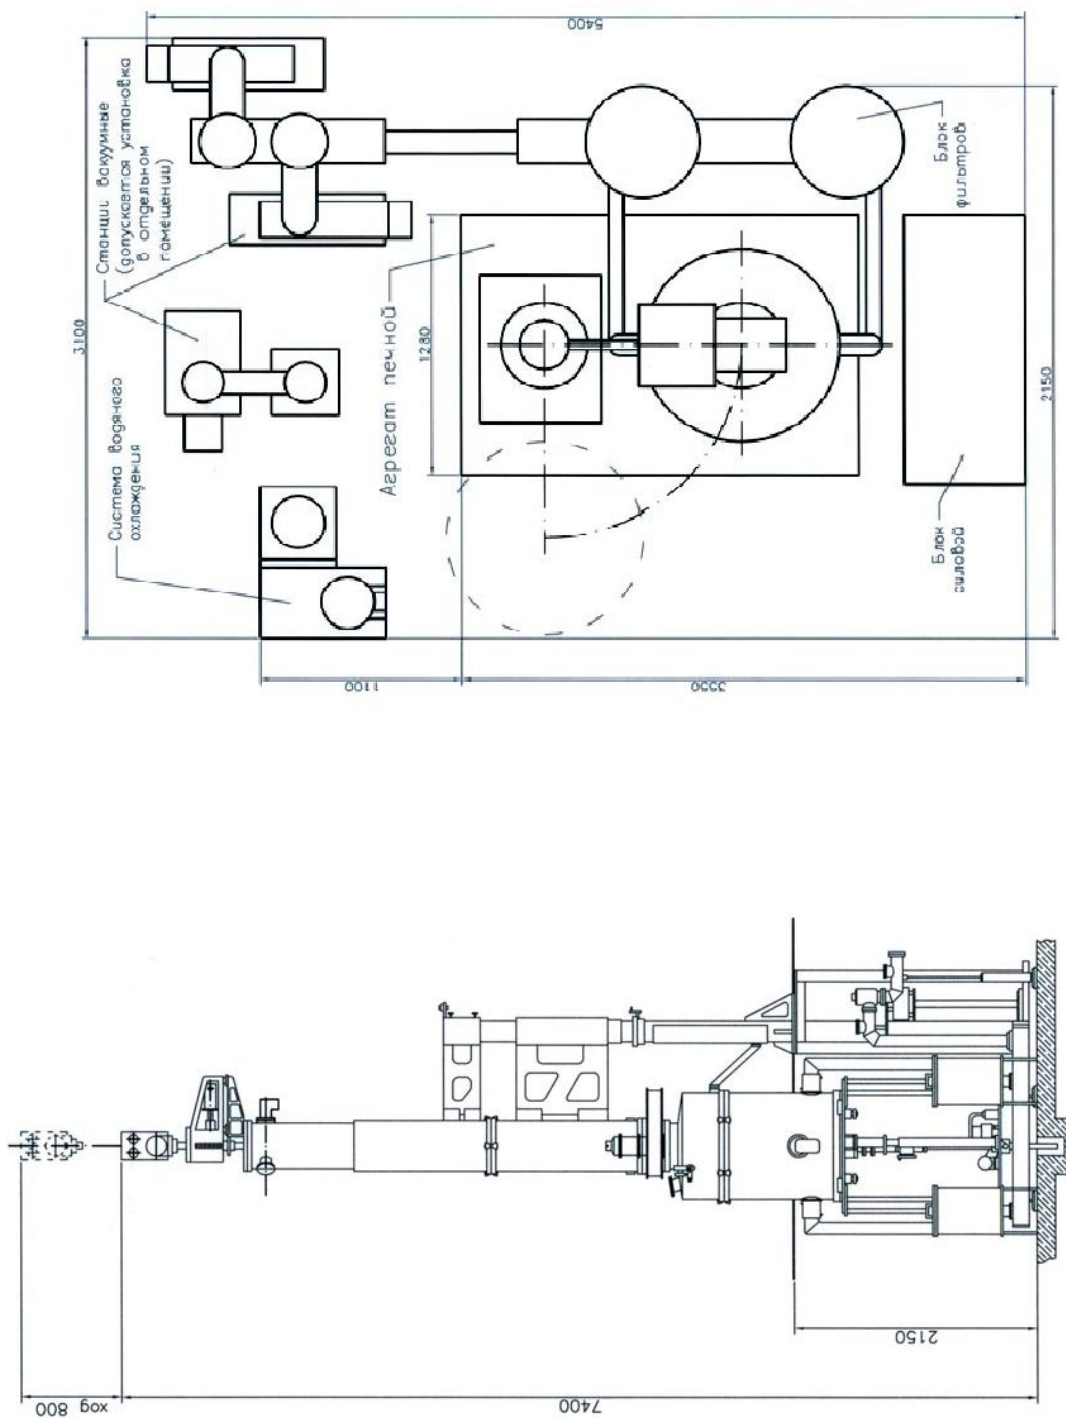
Установка «Редмет-90М», габаритный чертеж
